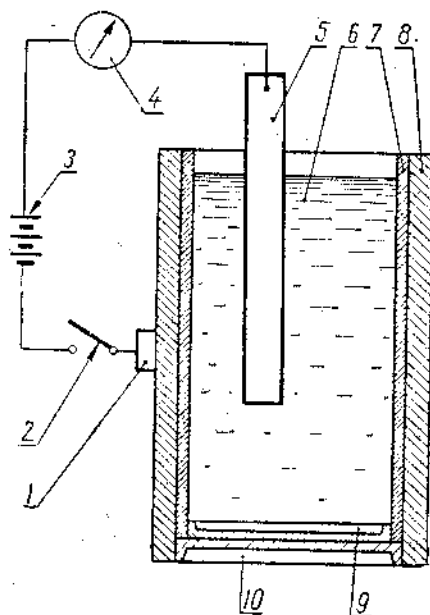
Приспособление для проверки качества сварных швов электролитическим способом.
